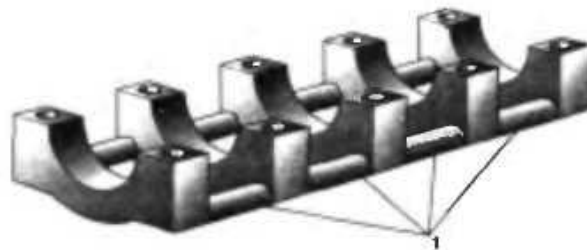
Кришка корінних підшипників, виготовлена як одна деталь:
